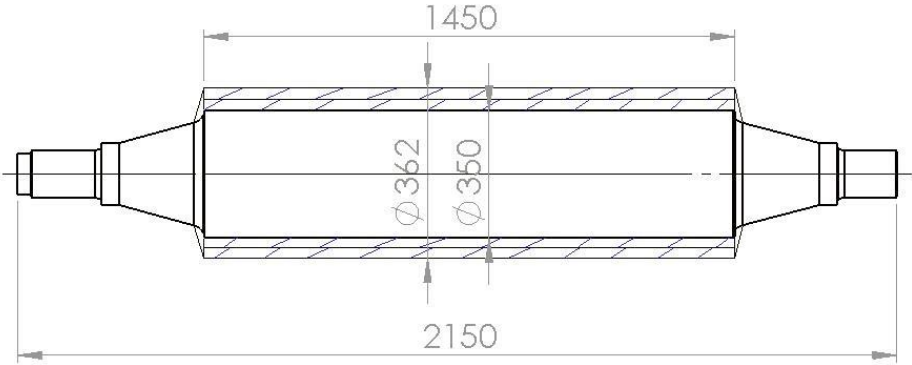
rechargement pièce $\varnothing 362$ mm avec fil weld clad 75
